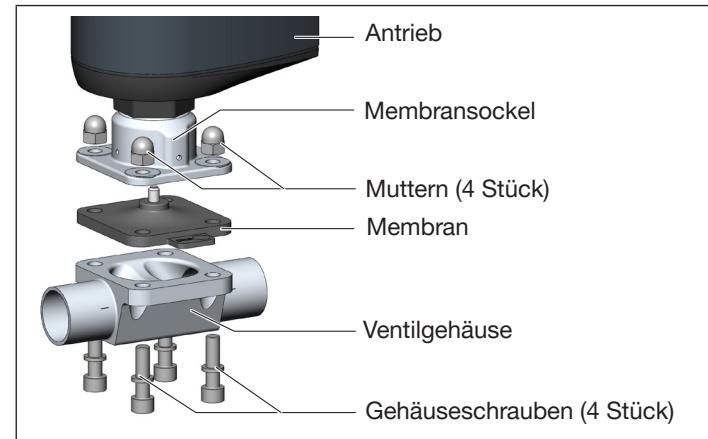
Demontage der Membran am Beispiel 2-Wege-Gehäuse
